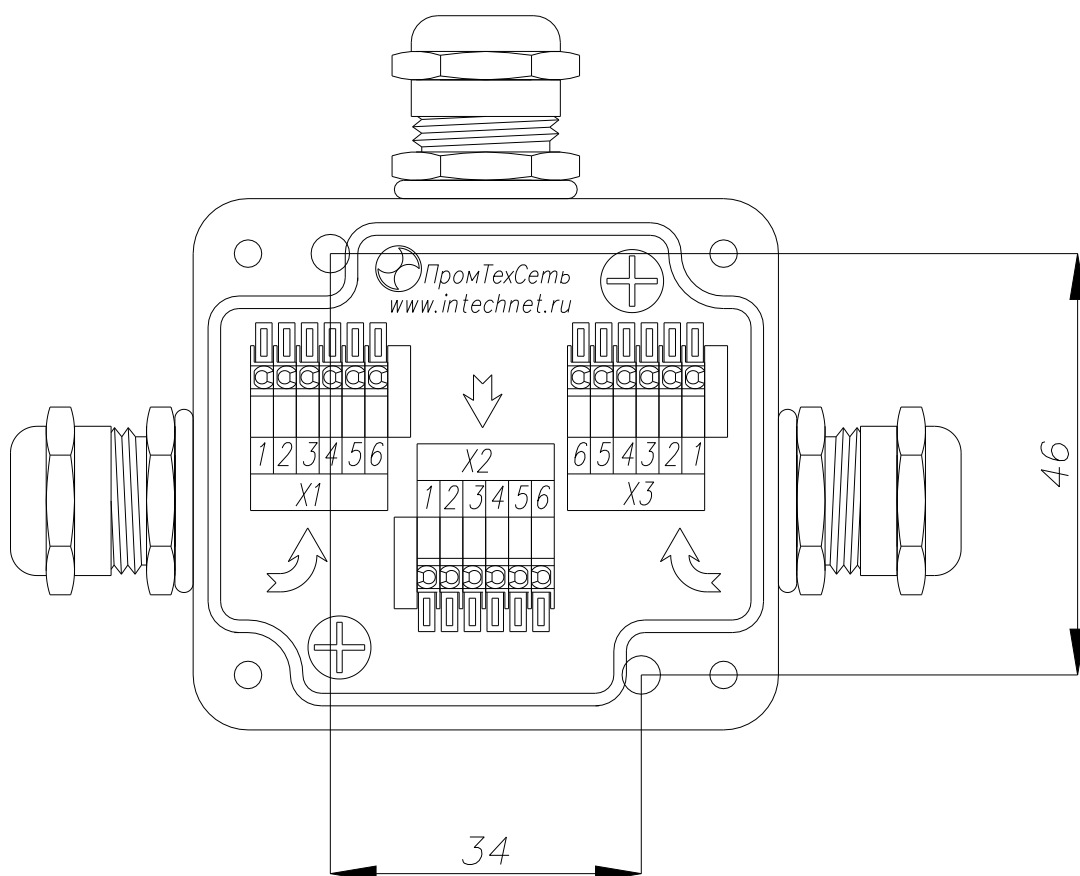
Компоновка и разметка места установки разветвителя РПМ-3
